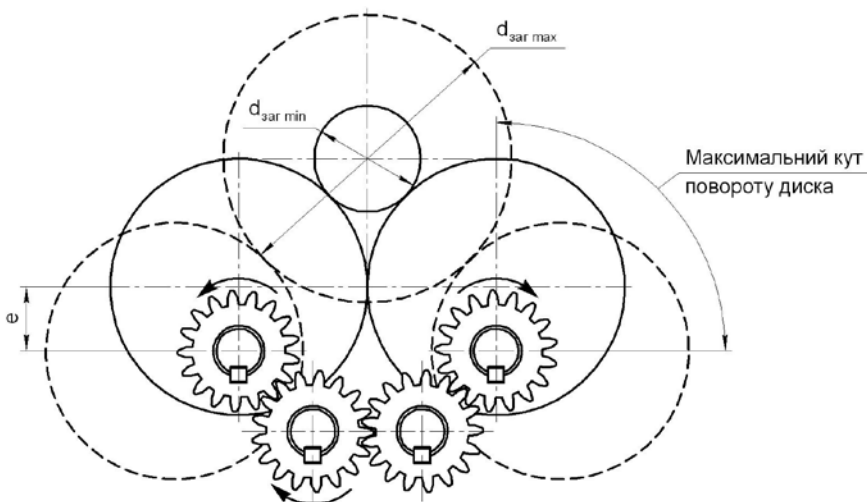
Схема механізму регулювання установлювальних елементів базуючої призми (патент України № 31416)
